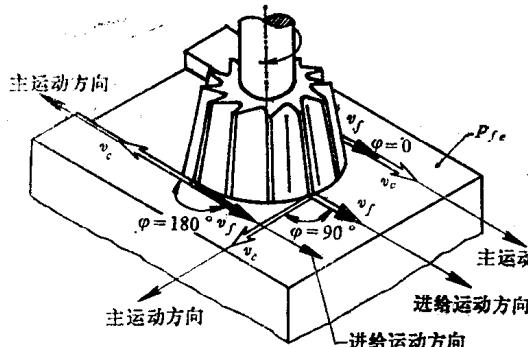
刀具和工件的运动——直柄单角立铣刀切削刃的三个选定点
